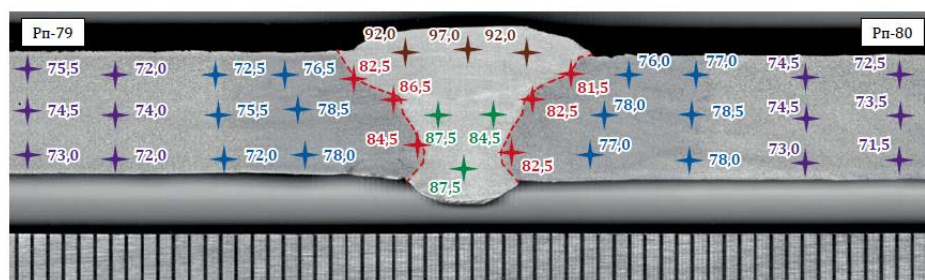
Схема измерения твердости в области стыкового сварного соединения
